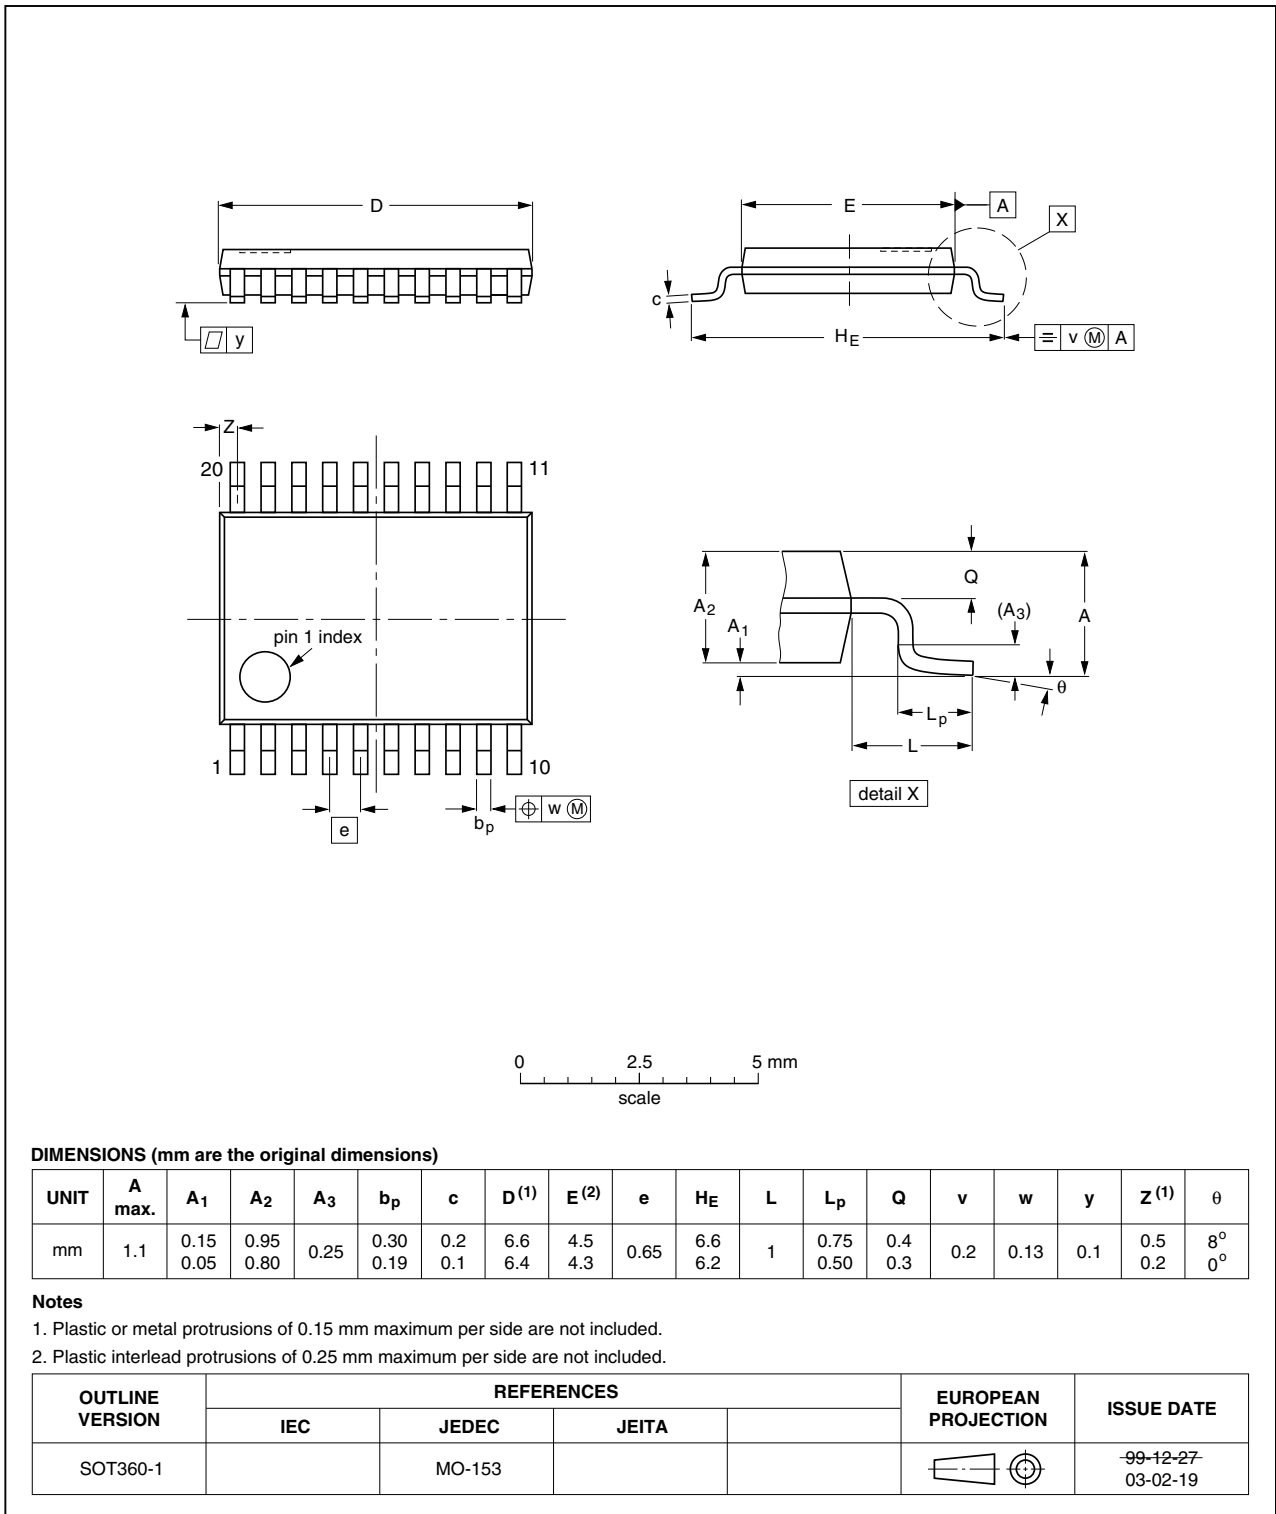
封装尺寸 SOT360-1 (TSSOP20)
